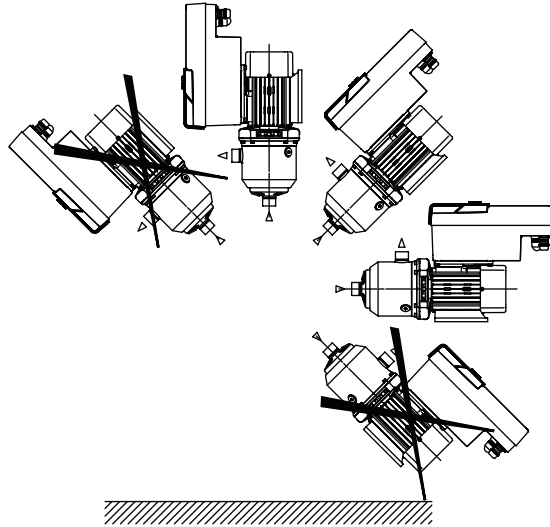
Tilladte installationspositioner med motoraksel og elektronikmodul, der vender opad (0°)
